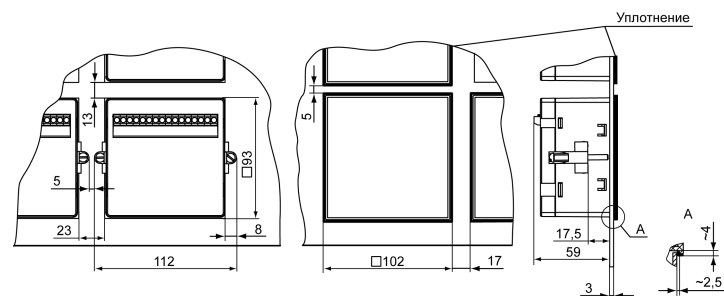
Прибор в корпусе Ц1, установленный в щит толщиной 3 мм
